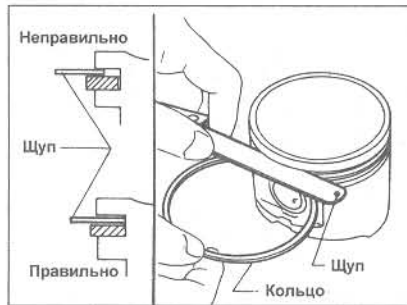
Проверка бокового зазора поршневого кольца (Глава 9)
